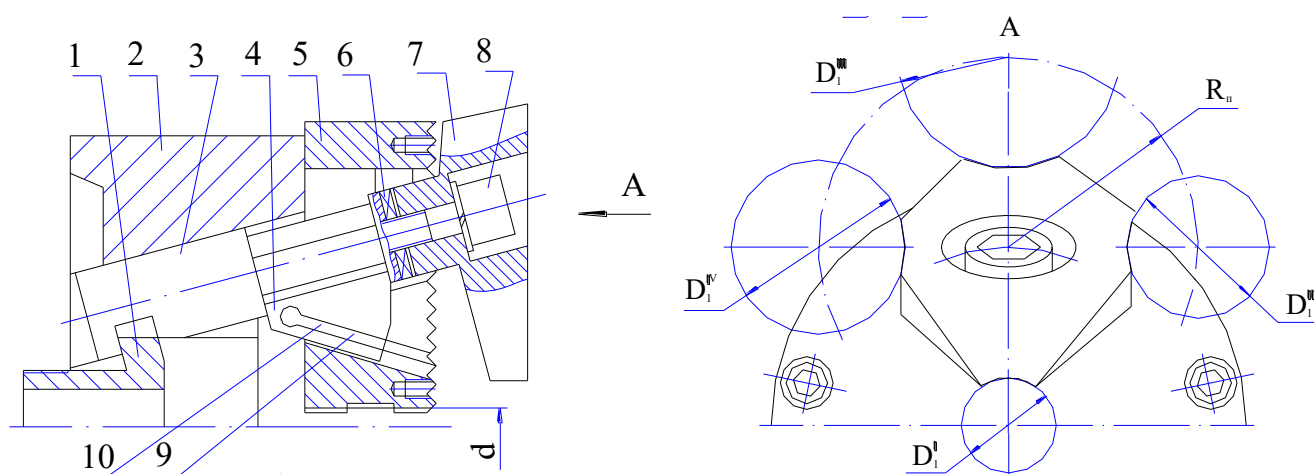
Широкоуніверсальний токарний патрон плунжерного типу із змінними позиційними багатопрофільними затискними елементами
